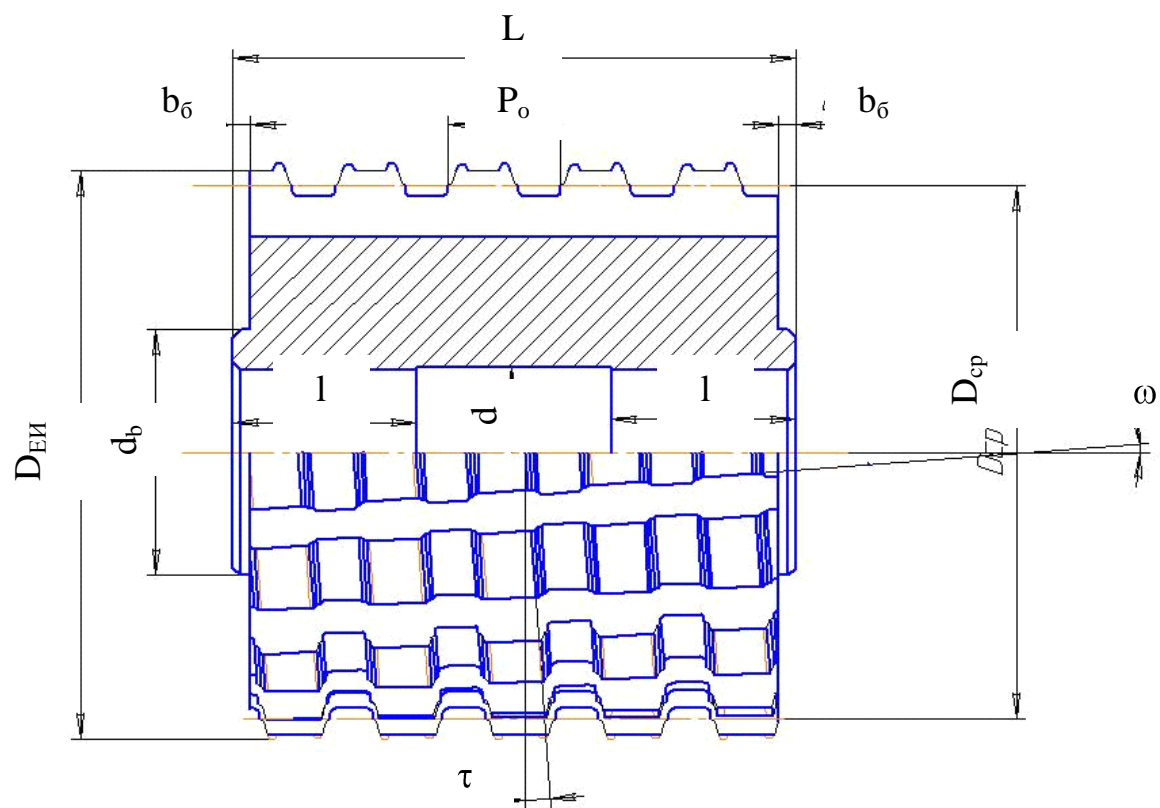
Основные конструктивные параметры червячной шлицевой фрезы
